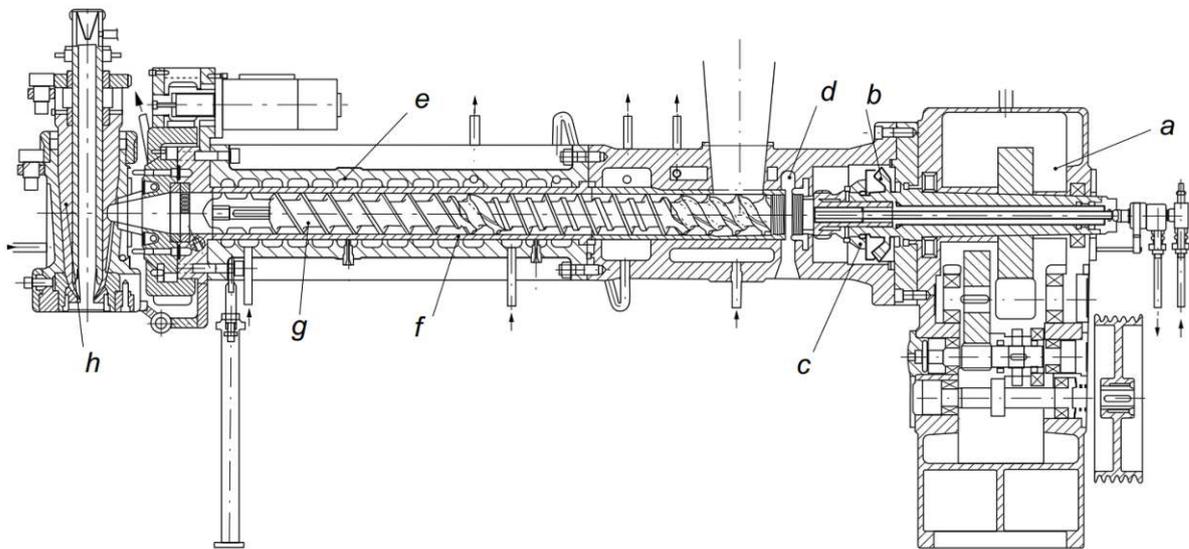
Technische Zeichnung eines Schneckenextruder samt Querspritzkopf.
